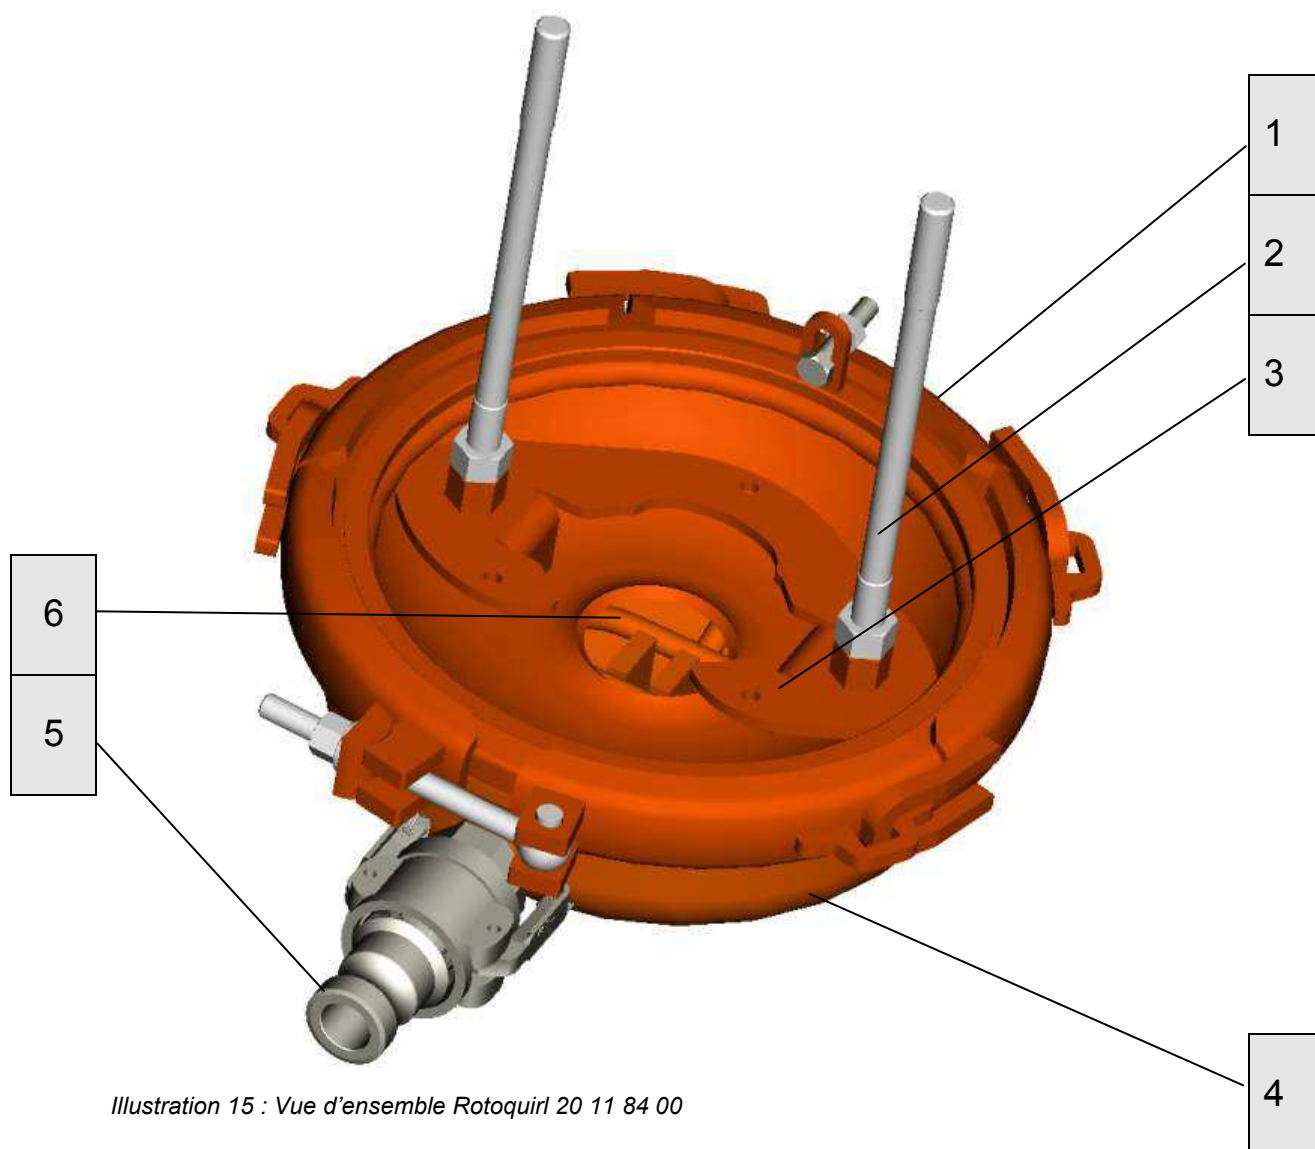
Vue d'ensemble Rotoquirl 20 11 84 00
